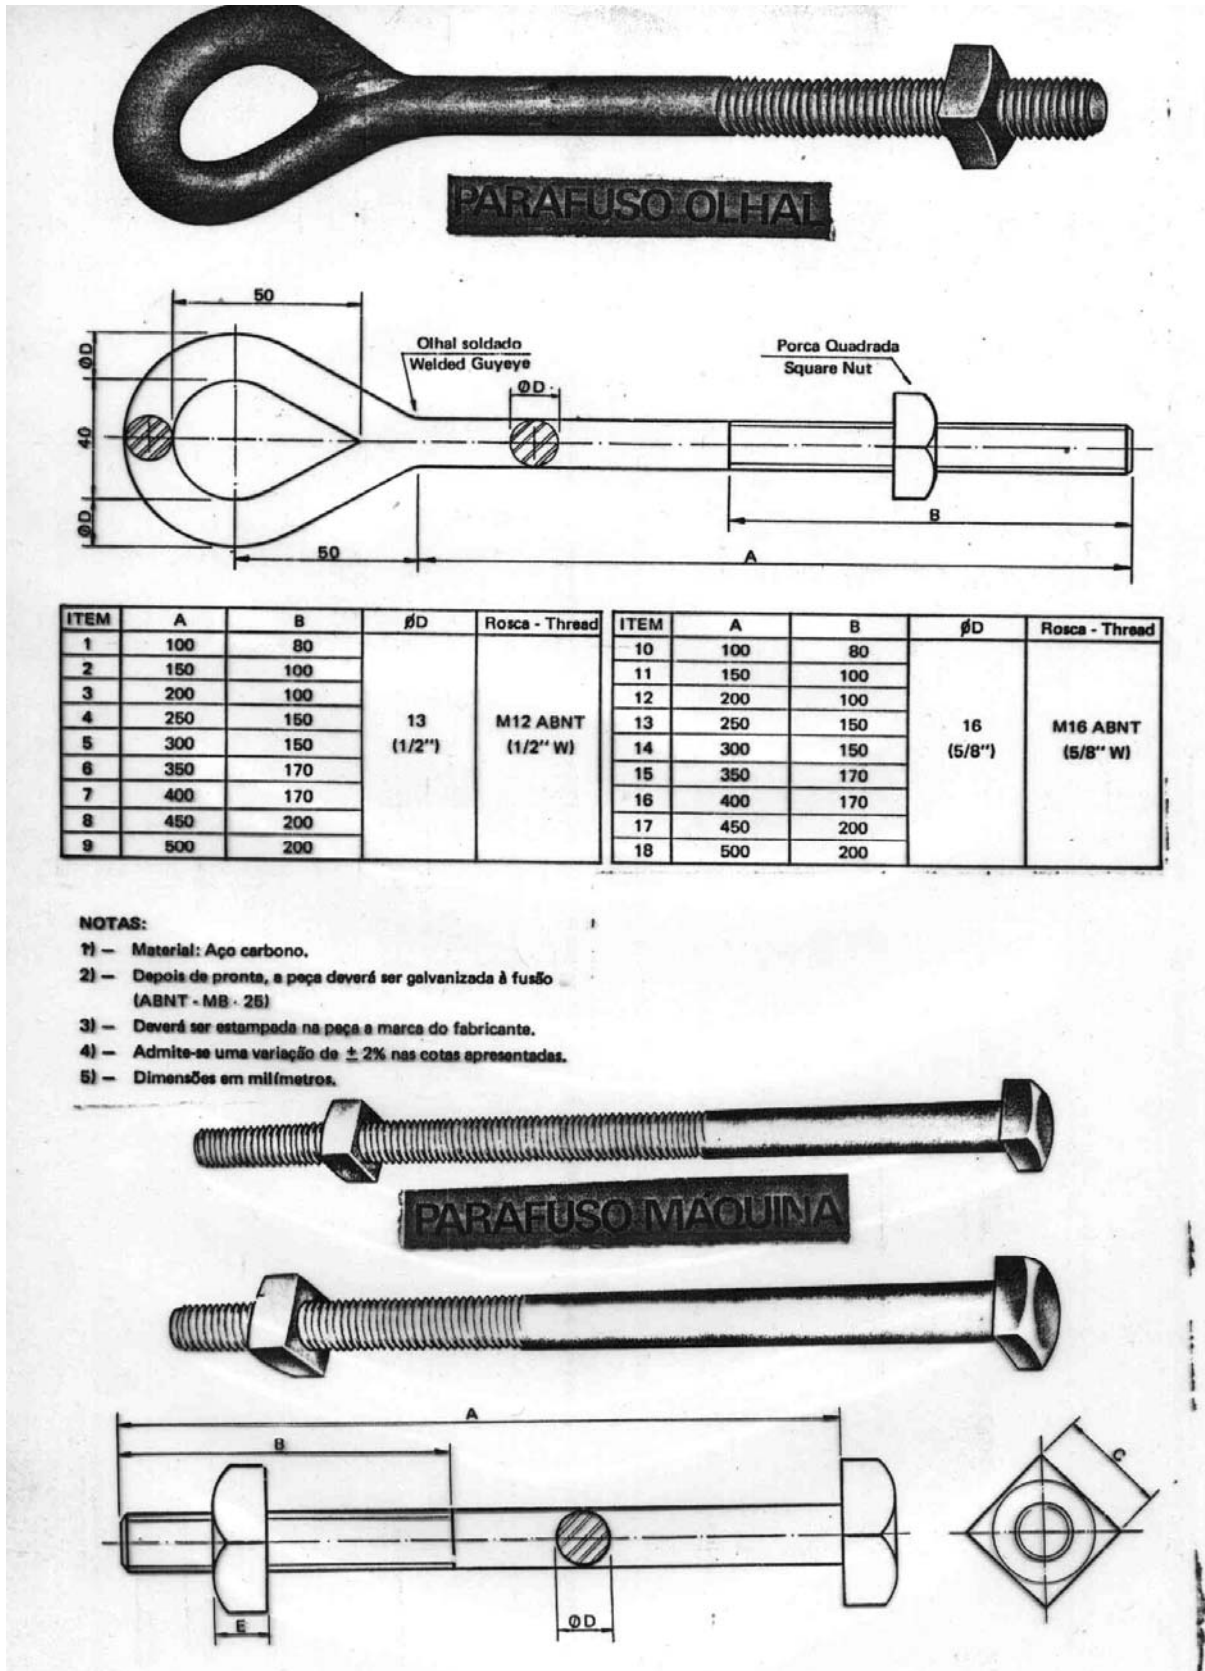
Dimensões de Parafuso Olhal e Máquina
